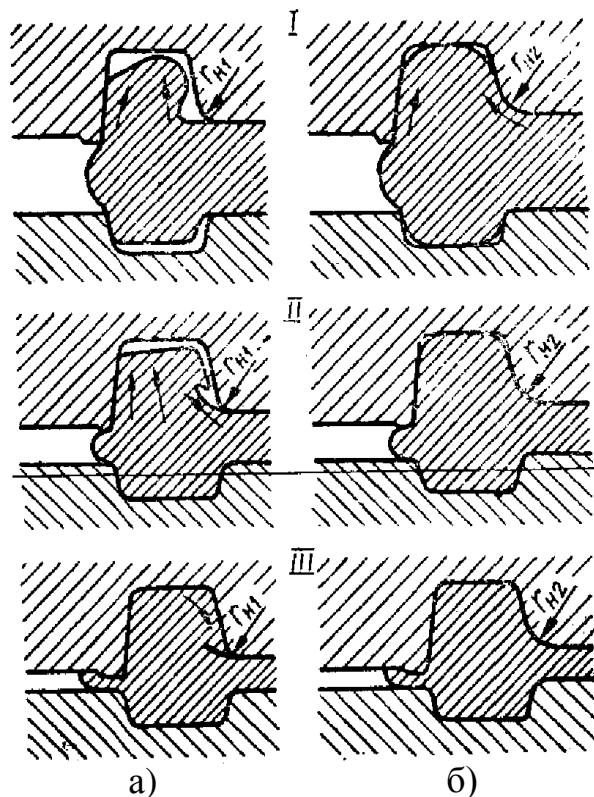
Схема плину металу при деформуванні штампуємої поковки:
